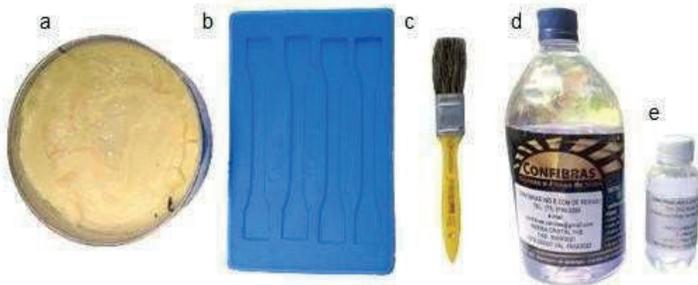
a) Cera Desmoldante b) Molde de Silicone c) Pincel d) Resina Poliéster e) Catalisador.
